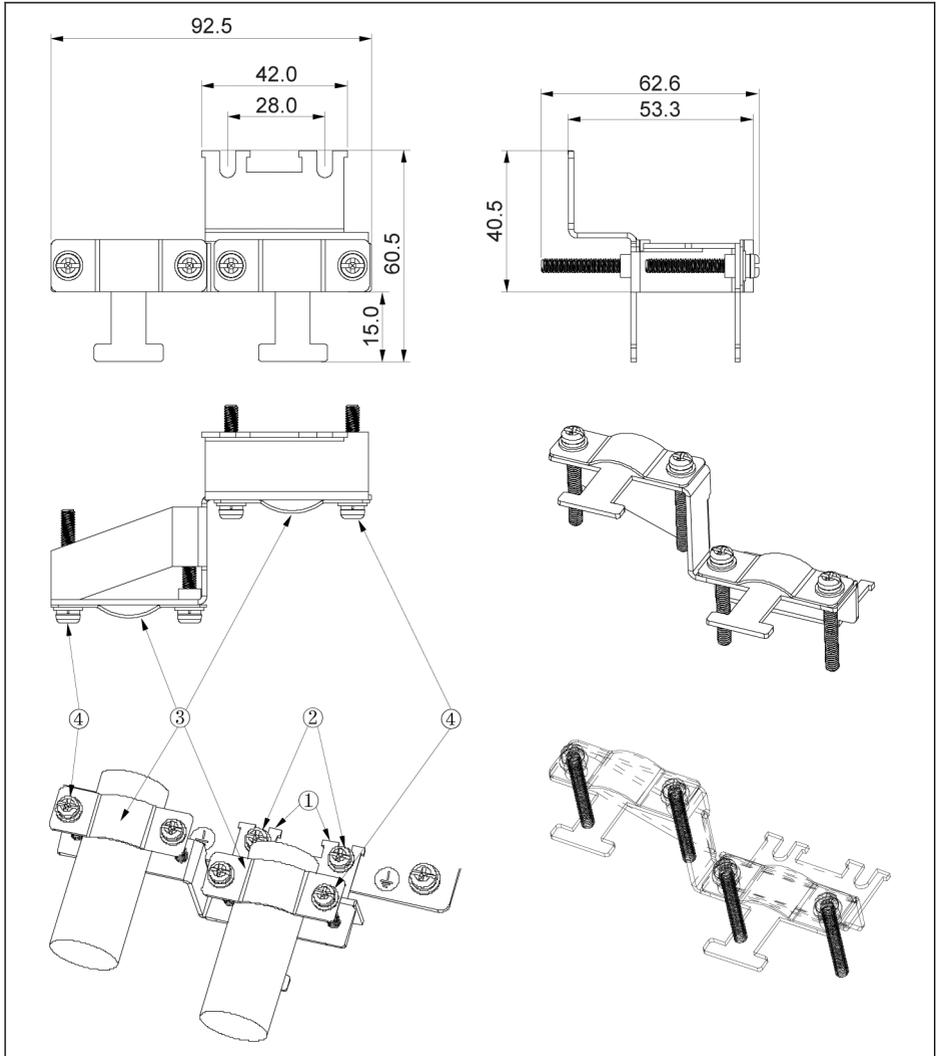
Conexión del cable apantallado con accesorios para 5K50...22K0
